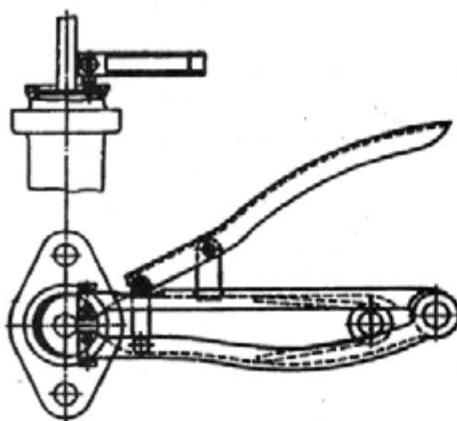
Круглогубцы для монтажа и демонтажа стопорного кольца главного цилиндра сцепления и тормоза
